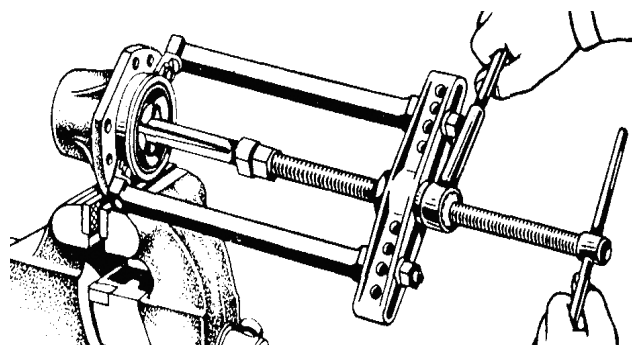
Выпрессовка внешней обоймы подшипника № 7607У из стакана ведущей шестерни.
